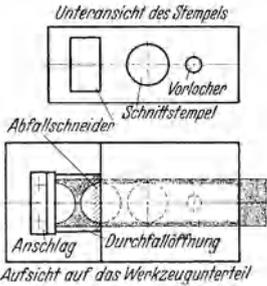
Schnittwerkzeug mit Abfallschneider.
